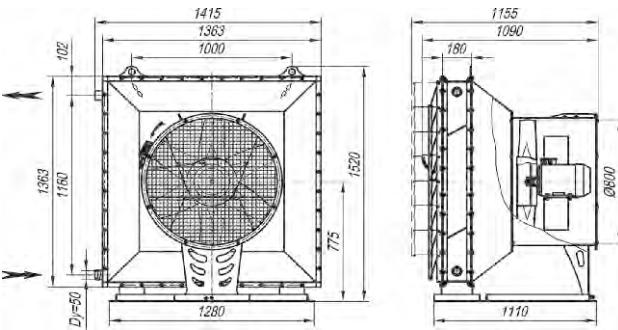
Габаритные и присоединительные размеры агрегата СТД-300 на базе водяного воздухонагревателя типа КСк.
